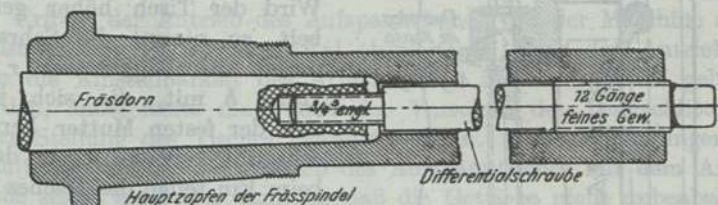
Einspannen des Fräfers mit einer Unterschiedsgewindeschraube.
